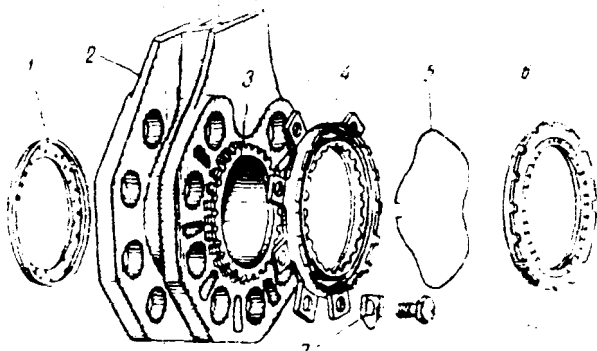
Схема бокового уплотнения кривошипной головки главного шатуна и смазки пальцев прицепных шатунов: 1—заднее кольцо; 2—главный шатун; 3—втулка главного шатуна; 4—шлицевой замок; 5—пружинное кольцо; 6—переднее кольцо; 7—замок винта; 8—винт крепления шлицевого замка
